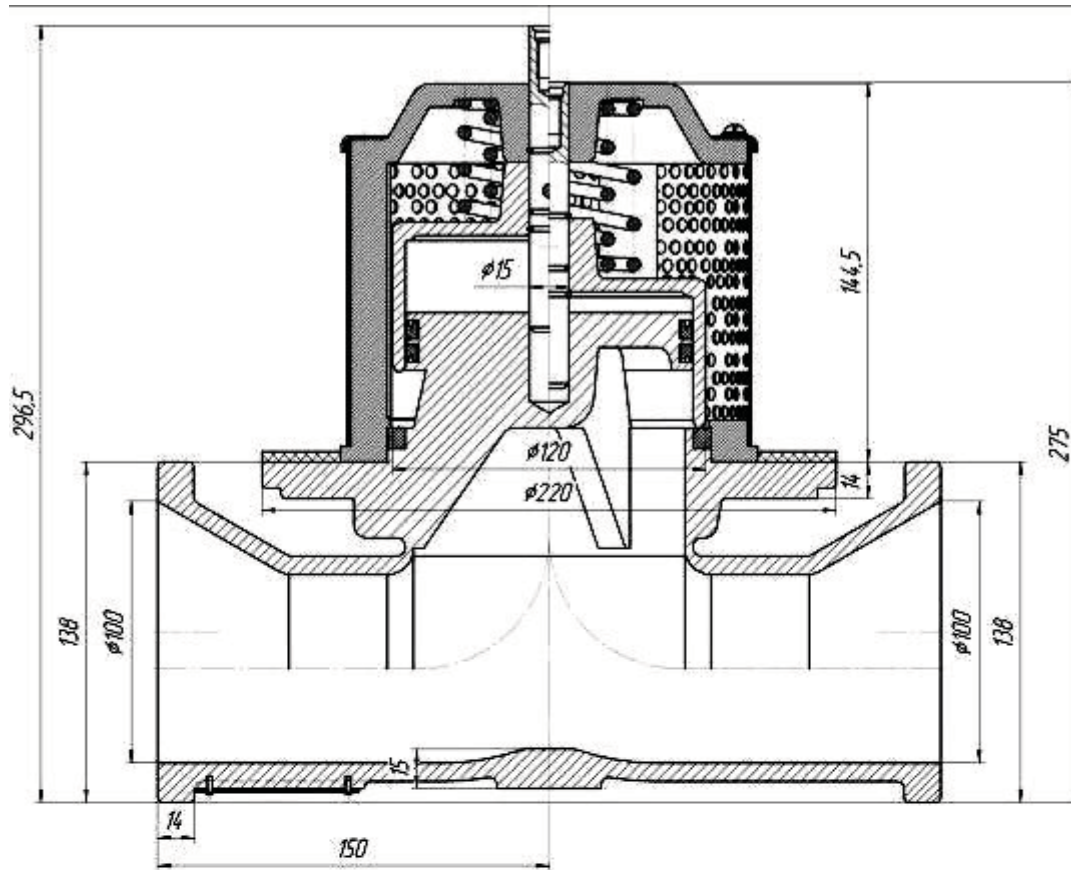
Типовой представитель: клапан донный пневматический Т-образный низкий профиль
